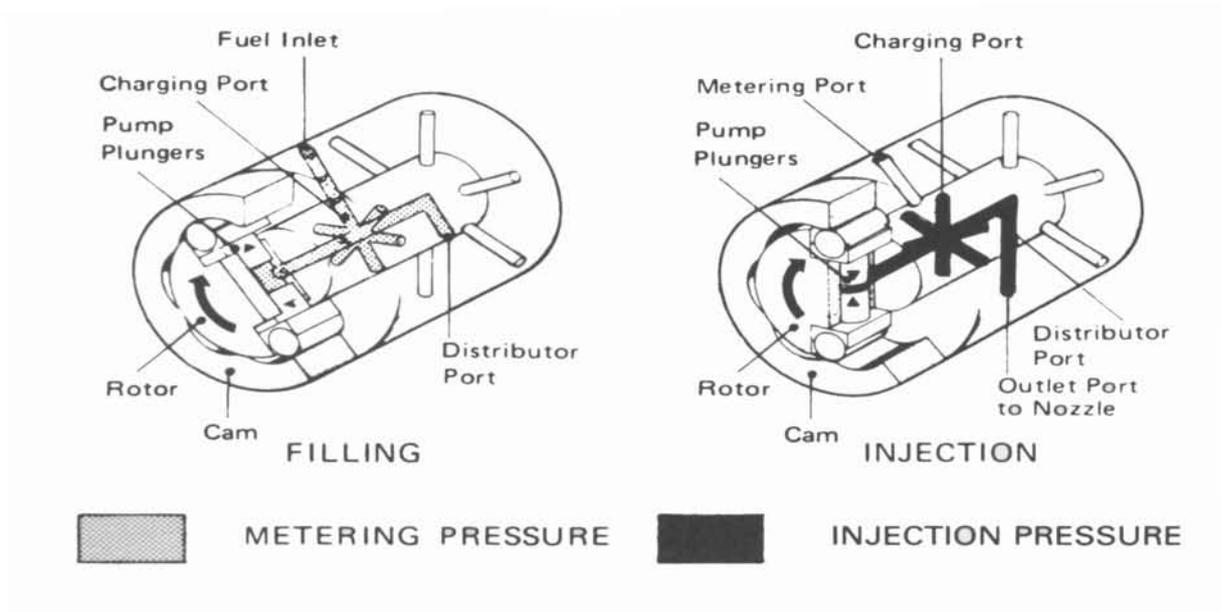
Rotor y bomba de alta presión de una bomba de combustible rotativa
